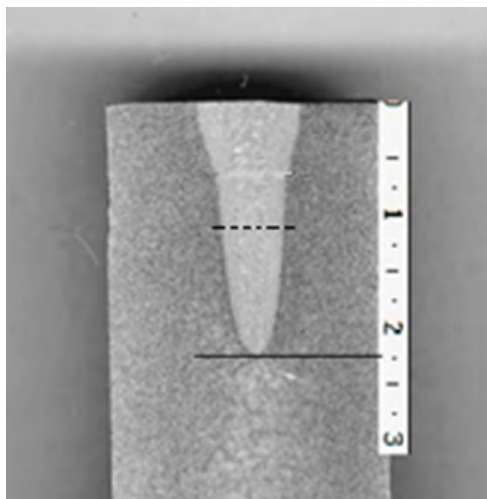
Образец формы шва низколегированной марганцовистой стали
